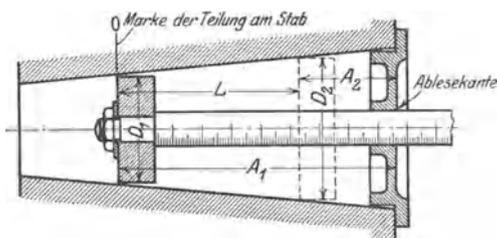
Meßvorrichtung für lange Hohlkegel.
